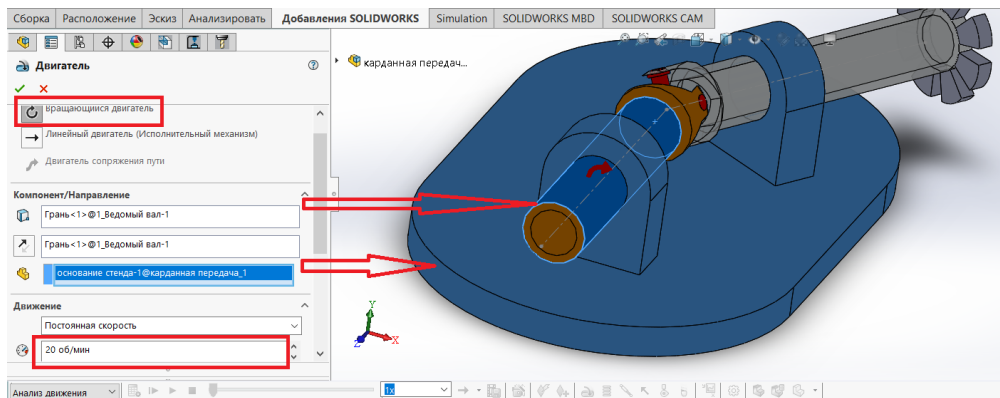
Назначение двигателя на ведущий вал карданной передачи
